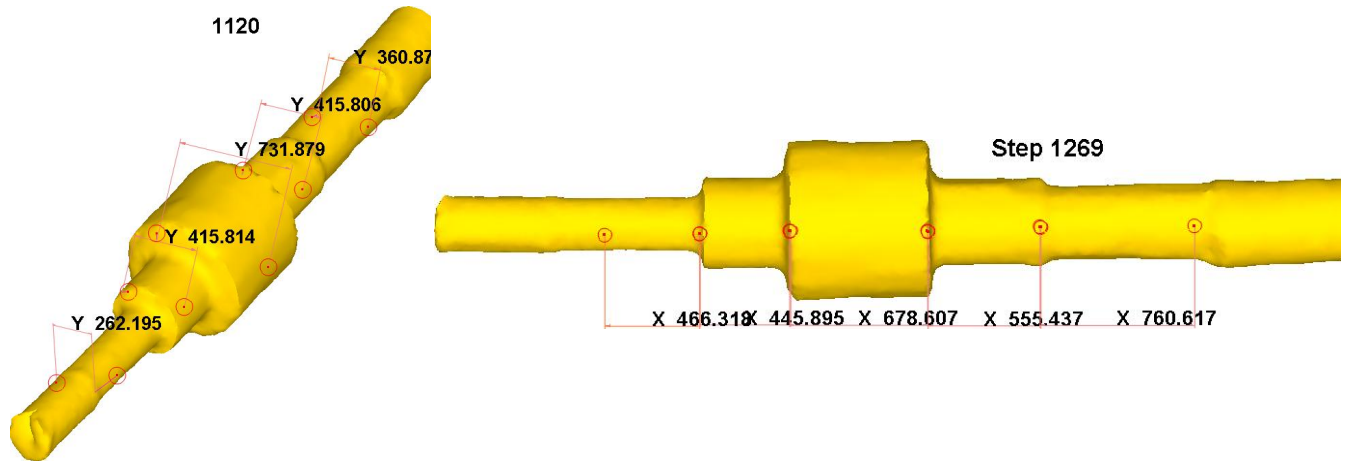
Внешний вид и размеры итоговой поковки
